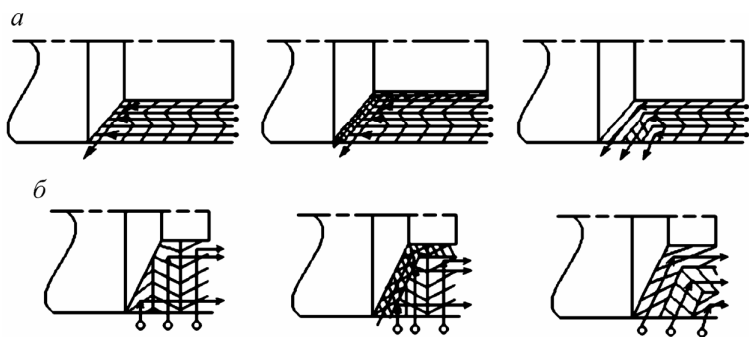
Схемы перемещений проходного (а) и подрезного (б) резцов при обработке основных форм поверхностей
